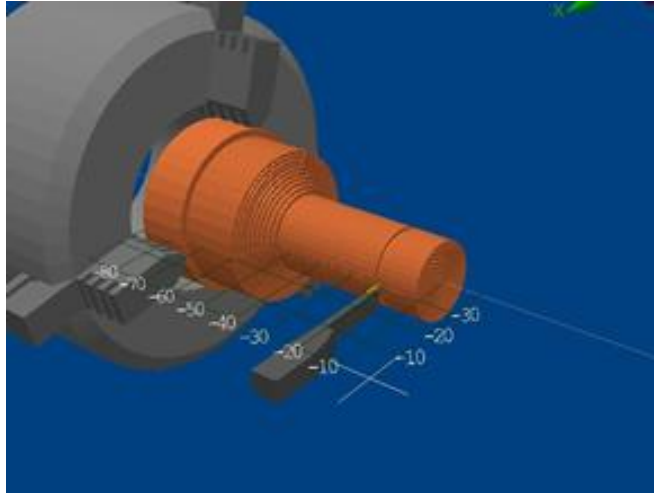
Підведення інструмента до заготовки, врізання інструмента
